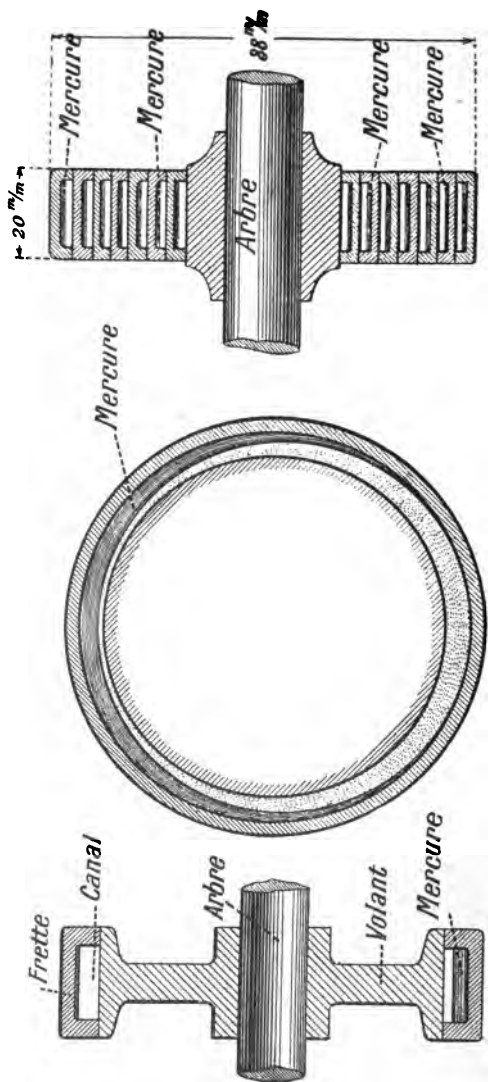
Compresseur rotatif Maurice Leblanc. Équilibrage automatique du rotor.
